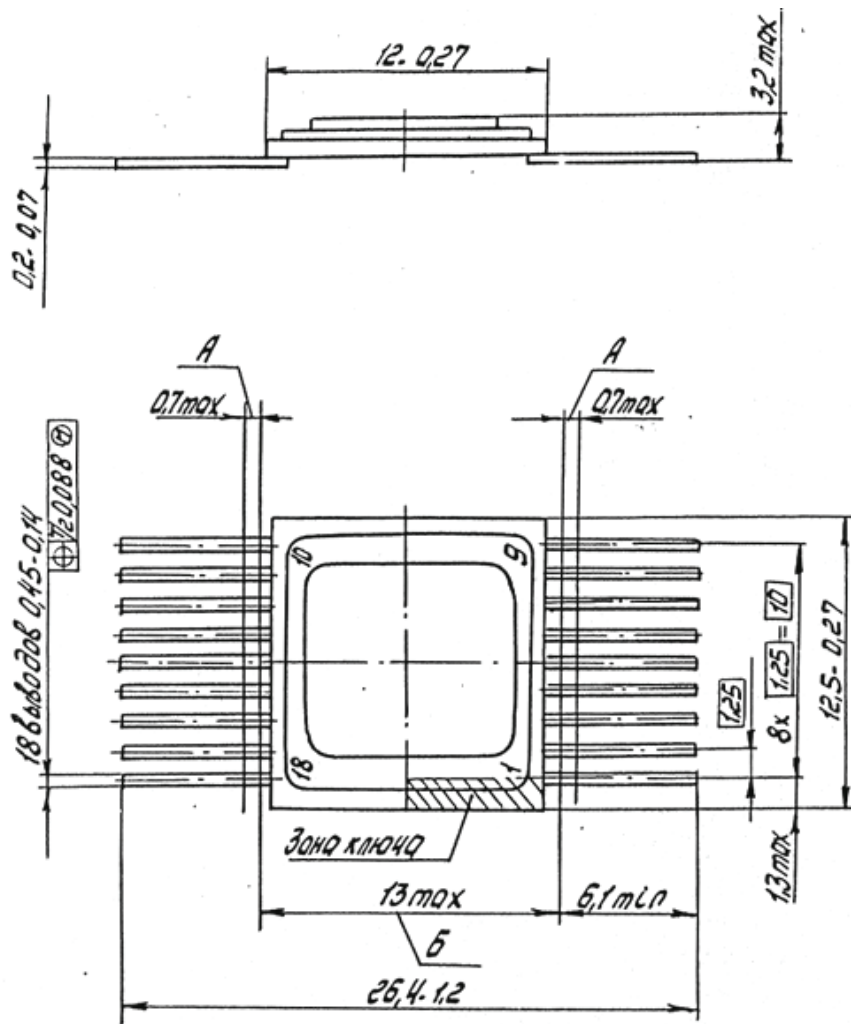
Габаритный чертеж корпуса 427.18-1.02
